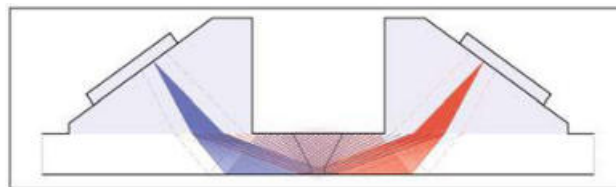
Схема контроля сварного соединения за один проход
